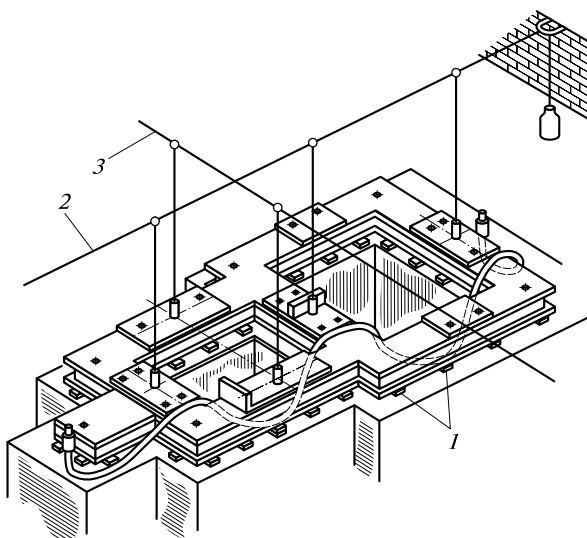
Укладка прокладок под фундаментные плиты:
